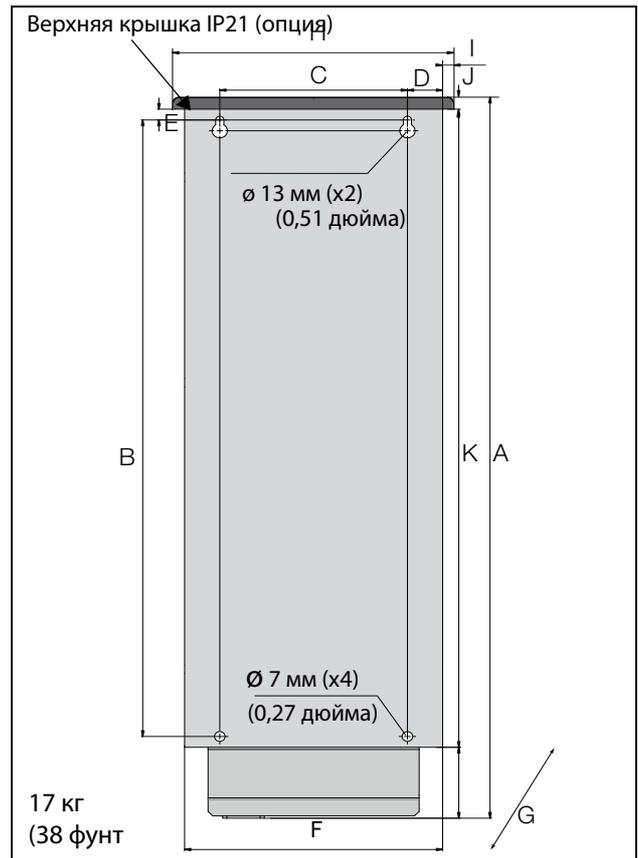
Устройство Emotron VFX моделей 48-025 по 48-058 (размер корпуса С2), модели 69-002 по 69-025 (размер корпуса С2(69)), вид сзади.
